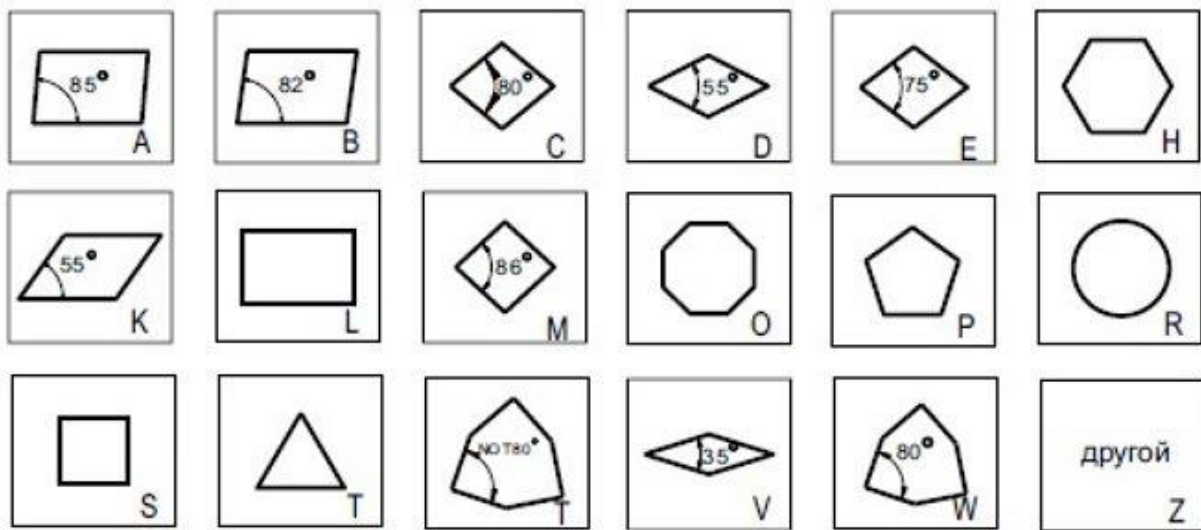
Формы твердосплавных пластин для резцов
